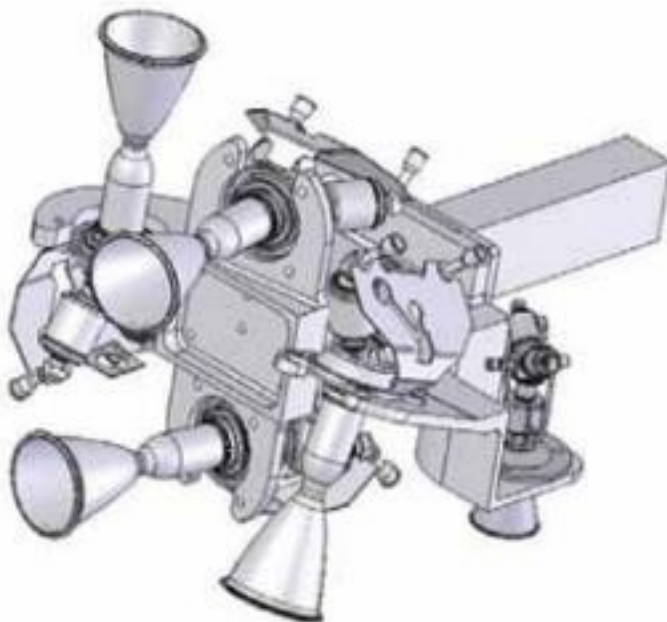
Внешний вид блока двигателей ПМ МВСК82.000.000 [7]
